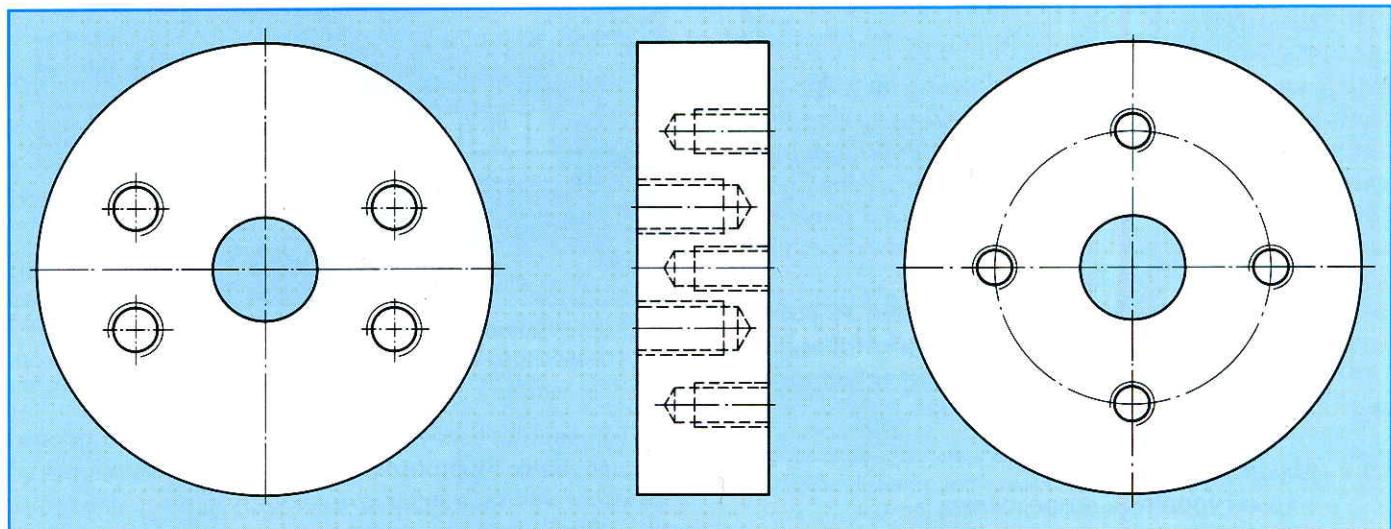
Неподвижное устройство для прохода трубопроводов в палубе
